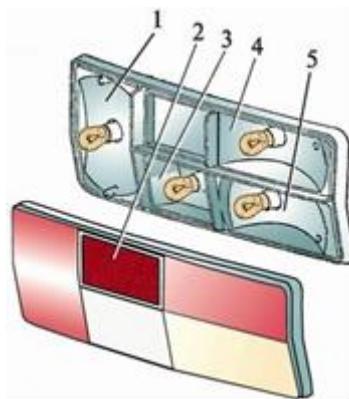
Задний фонарь: 1 – стоп-сигнал; 2 – световозвращатель; 3 – фонарь заднего хода; 4 – габаритный фонарь; 5 – указатель поворота
